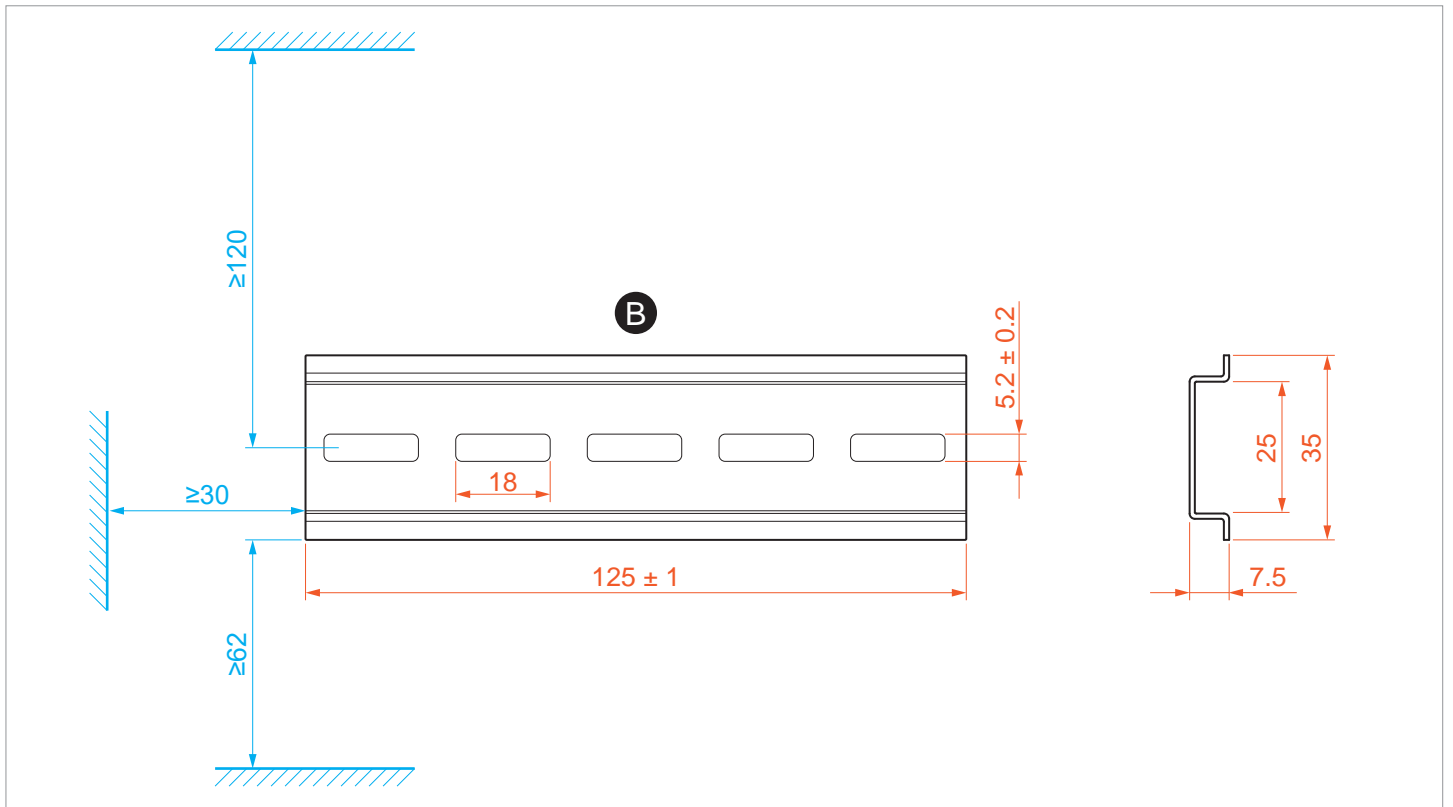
Dimensions et distances de montage du rail DIN (en mm)
